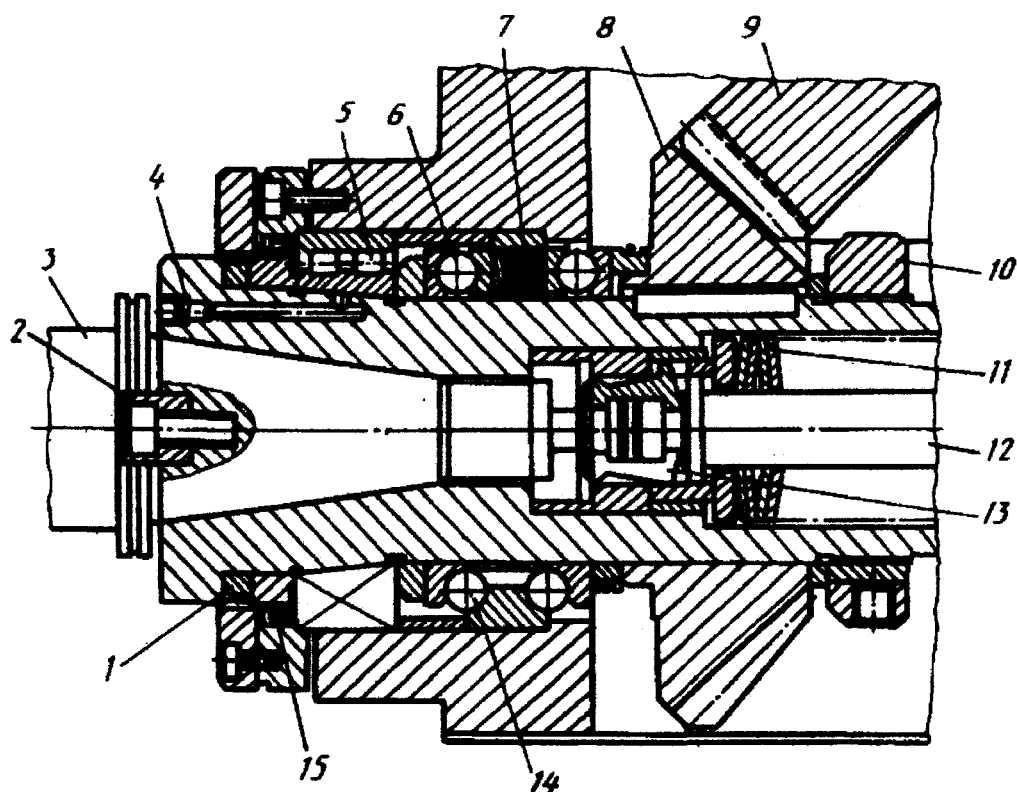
4. Передняя опора и конец шпинделя фрезерно - расточного станка с ЧПУ:
